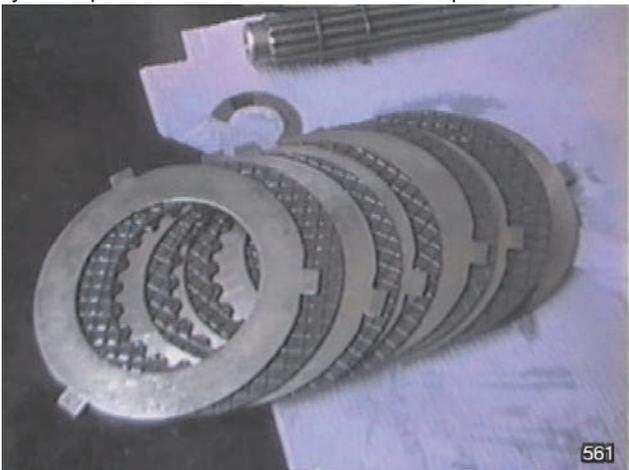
Examiner l'état d'usure des disques de l'embrayage.
